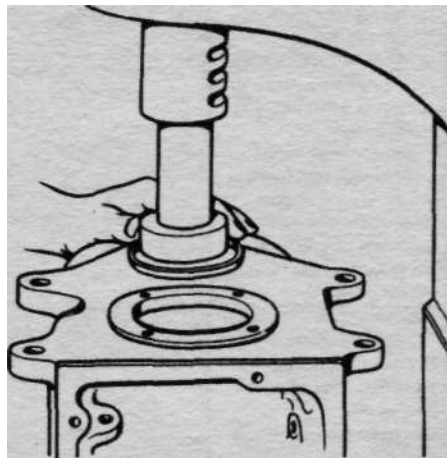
Запрессовка заглушки переднего подшипника промежуточного вала
